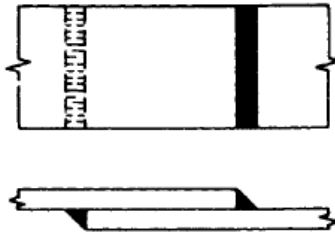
Las Tumpul (*Groove Welds*)
